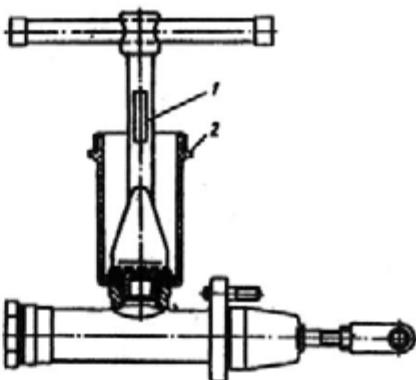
Вывертывание штуцера крепления бачка главного цилиндра специальной отверткой:
